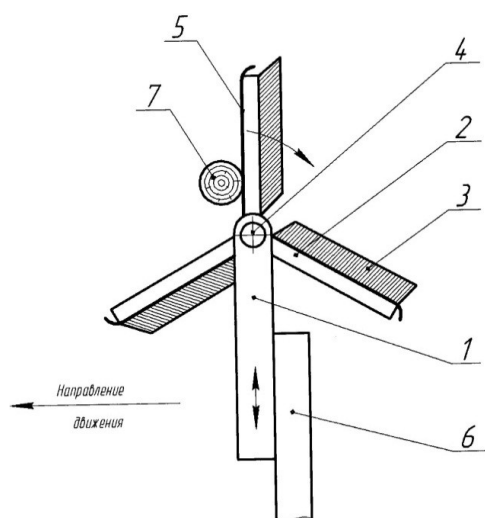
Схема устройства для обработки штамбовой зоны деревьев
